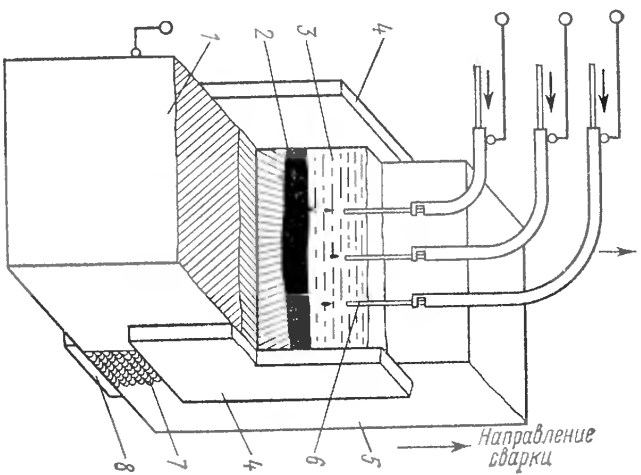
Схема электрошлаковой сварки:
